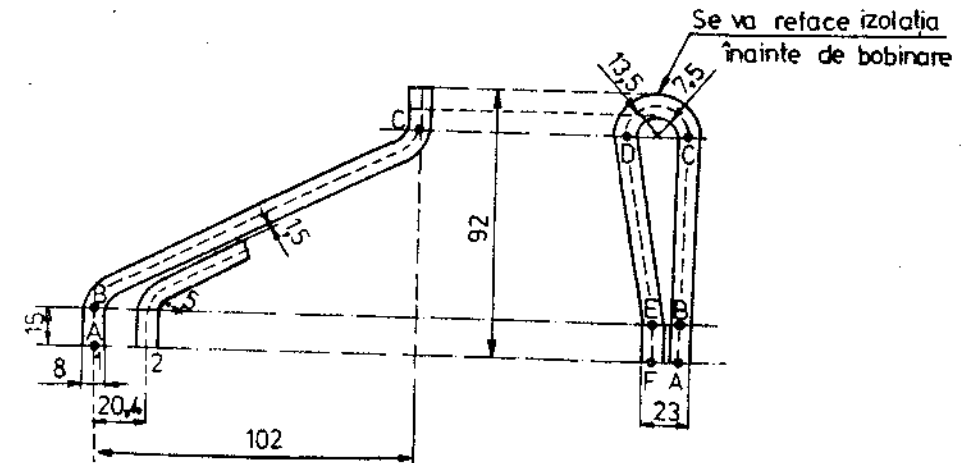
Dimensiunile capătului frontal al bobinei rotor.
